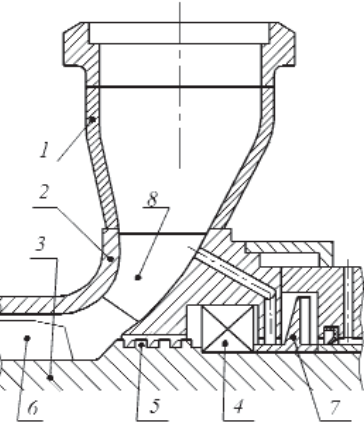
1 - входной патрубок, 2 - корпус, 3 - вал, 4 - подшипник, 5 - винтовой насос, 6 - предвключенный шнек, 7 - импеллер, 8 - пилоны
